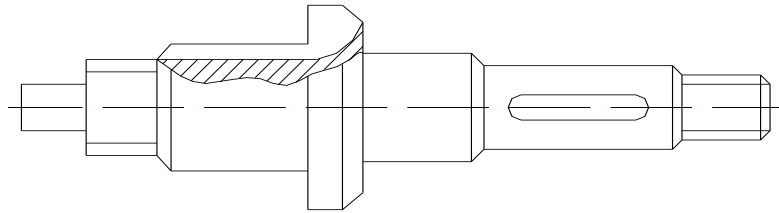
Конструктивна схема вторинного валу редуктора
